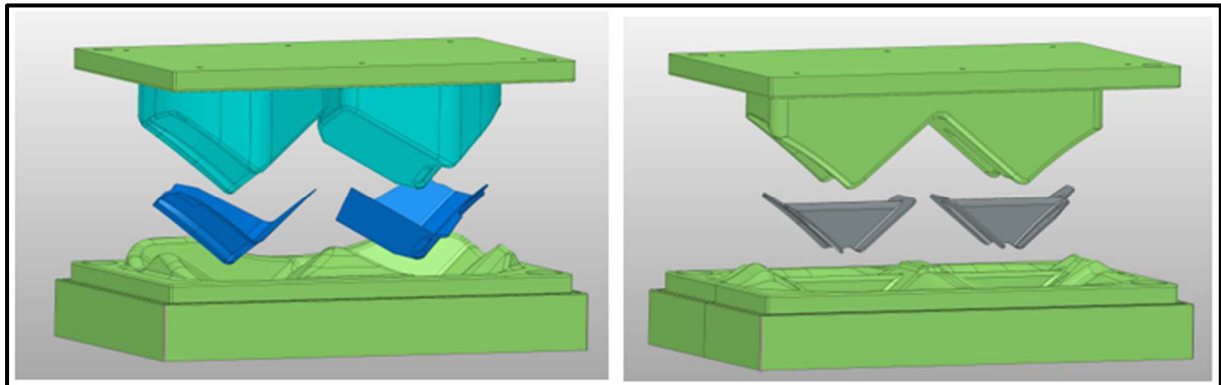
Aufbau Thermopresswerkzeug - Schale/ Rippe (rechts & links)/ 22.11.24 Lakowa intern.
